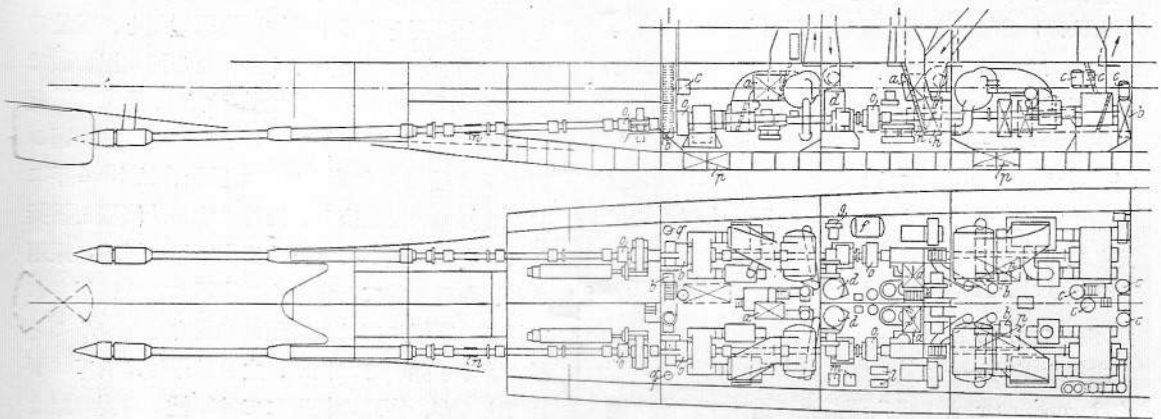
Kleiner Kreuzer „Königsberg“. Anordnung der Hauptmaschinenanlage (vier selbständige Getriebeturbinensätze auf zwei Wellen) und der Hilfsmaschinen
